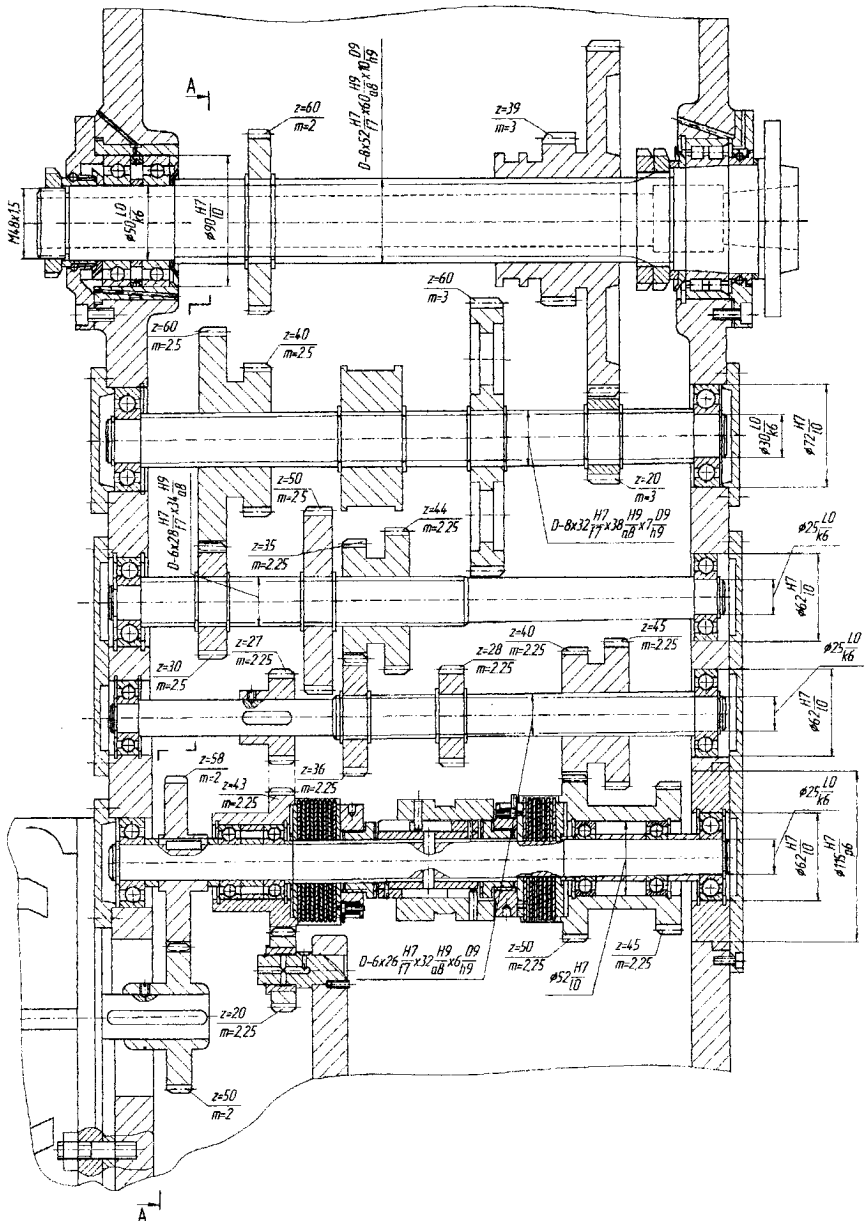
Розгортка поздовжнього перерізу коробки швидкостей токарної групи, зокрема токарно-револьверних
